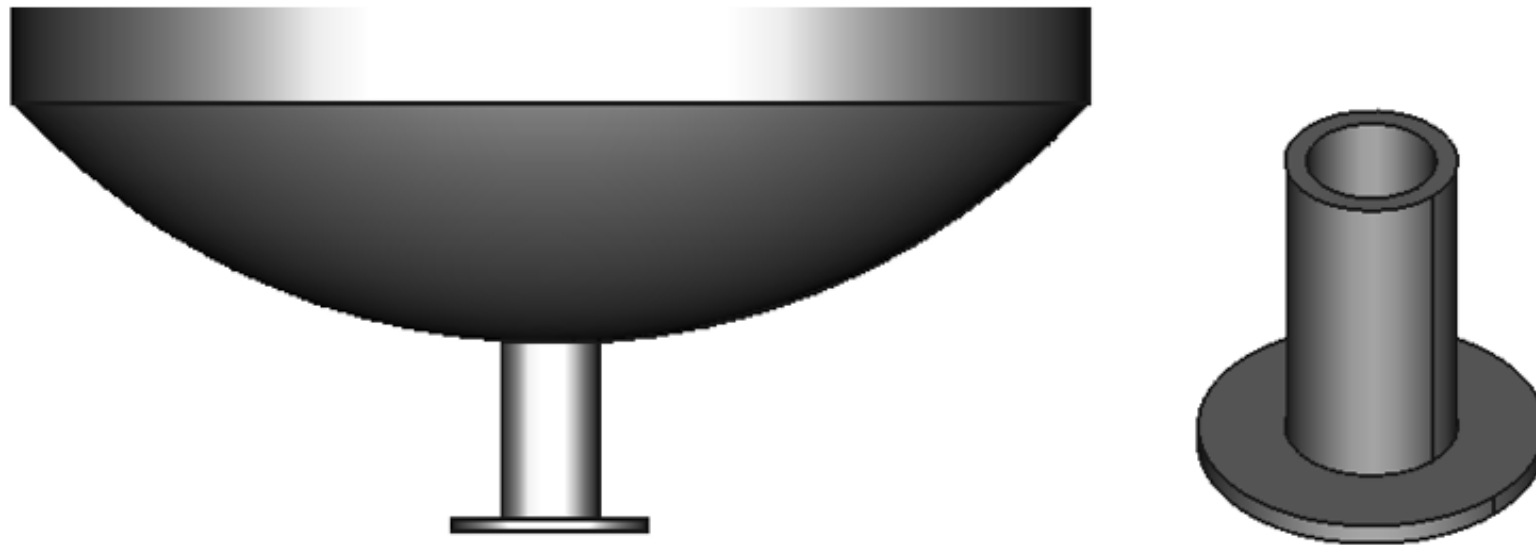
Vista de perfil de la tapa inferior y vista en alzado de la boca de salida
